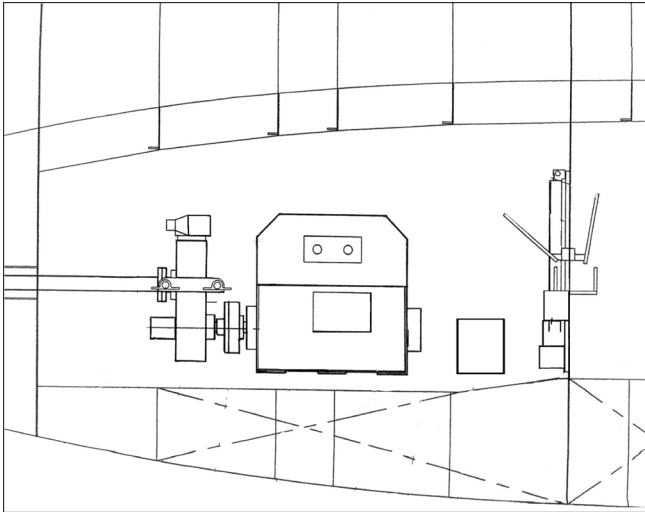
Beispiel ELBE: Teilansicht aus Maschinen-Raum-Plan
